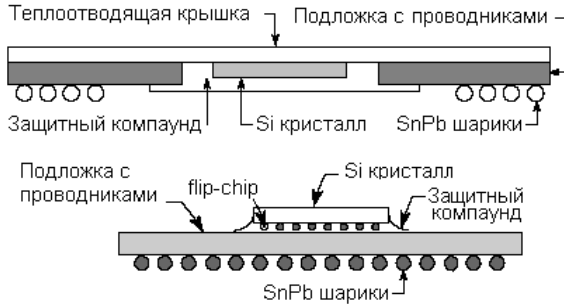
Конструкції мікросхем в корпусах типу BGA
